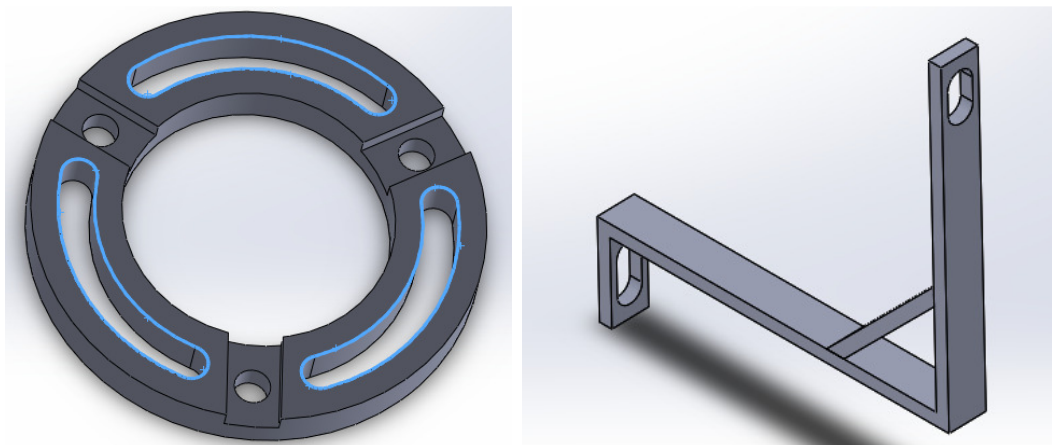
Elemento de Fixação entre Encoder – Máquina
